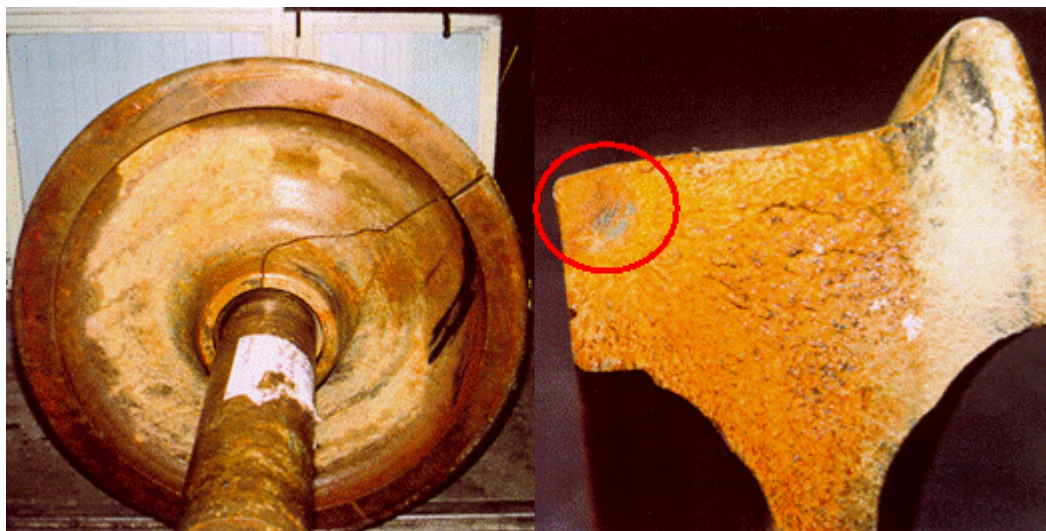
Rueda fracturada por el descarrilamiento de Stein-Säckingen (izquierda). Superficie final de fractura (derecha) con el inicio de la fisura crítica (círculo).
